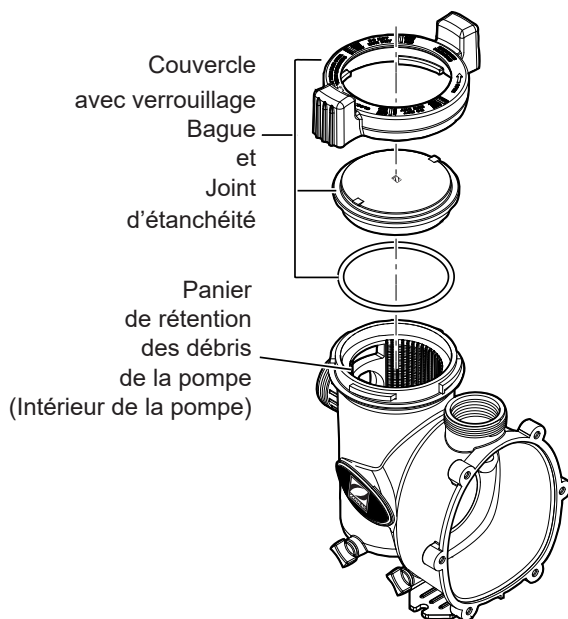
VUE ÉCLATÉE DE L'ASSEMBLAGE DU COUVERCLE
